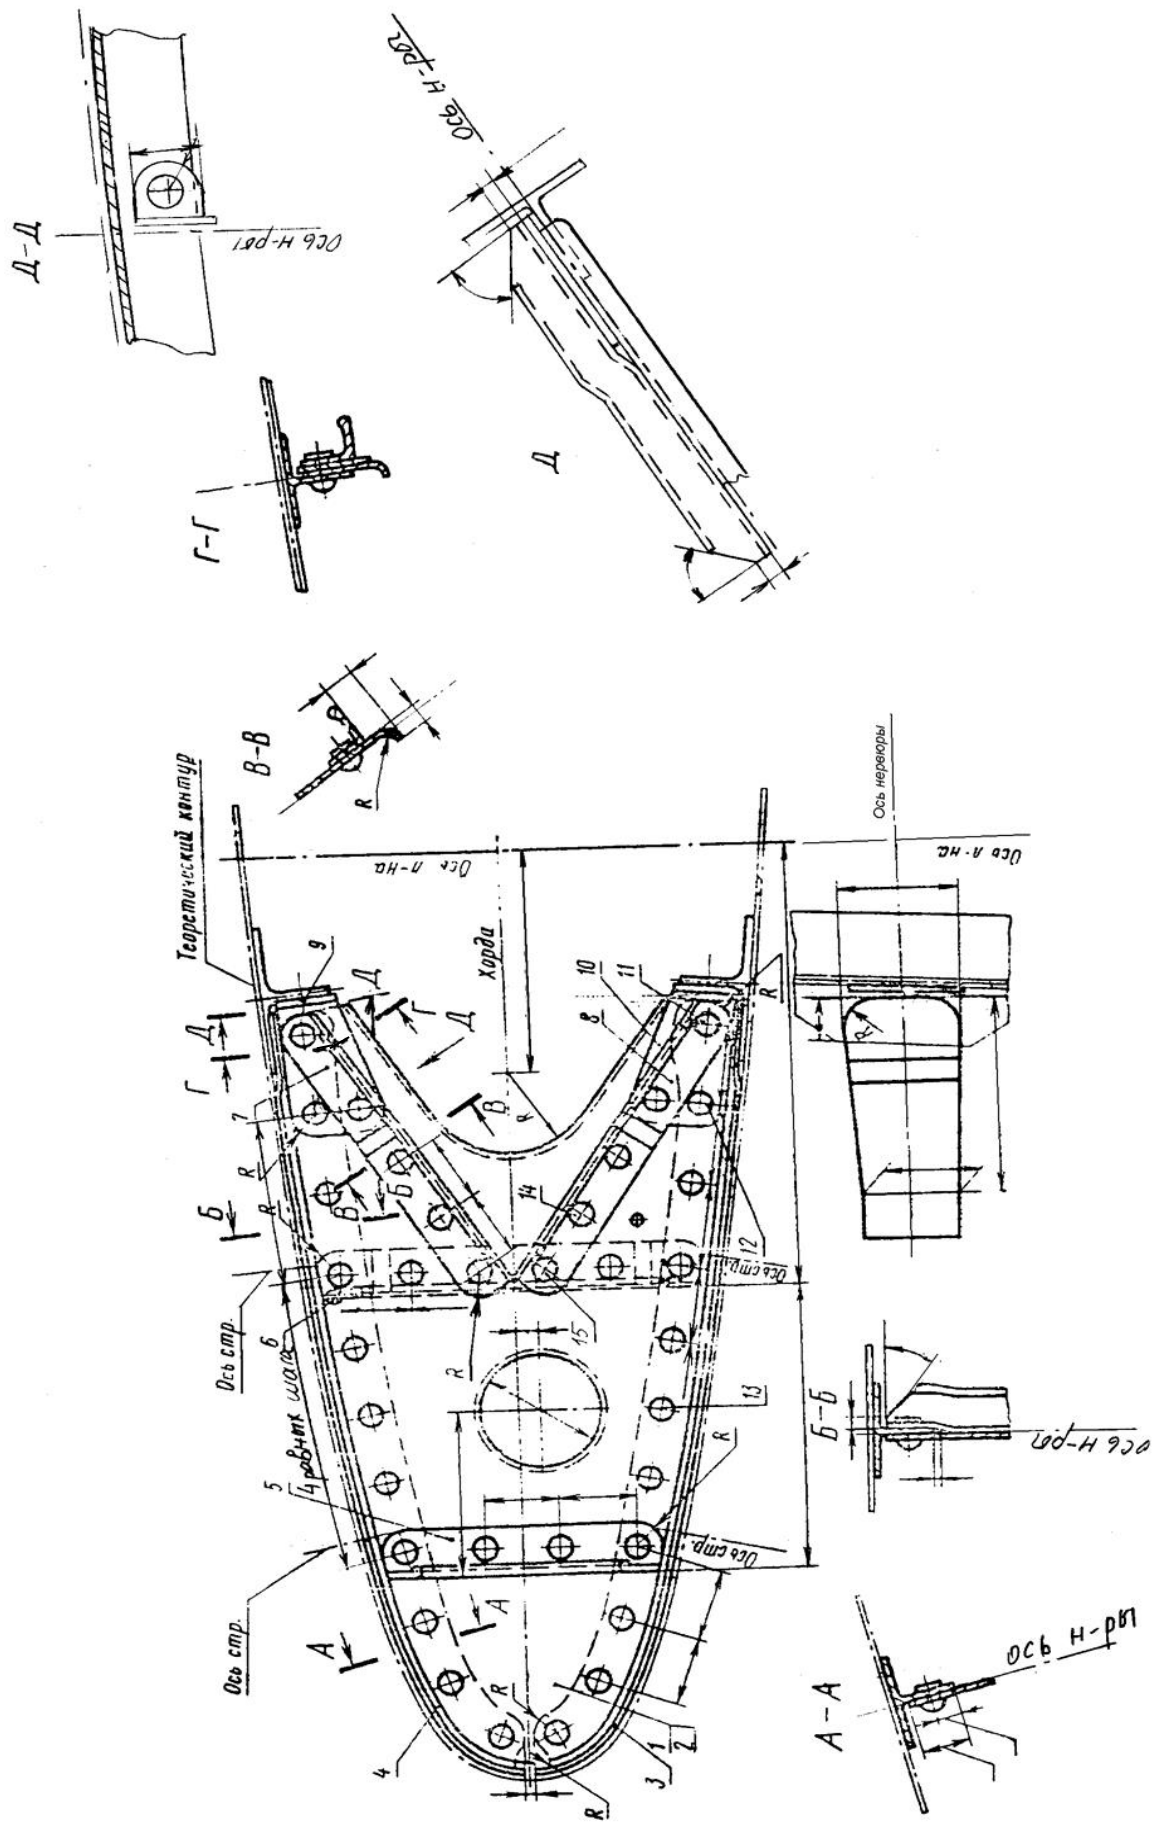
Пример выполнения сборного чертежа носка нервюры
